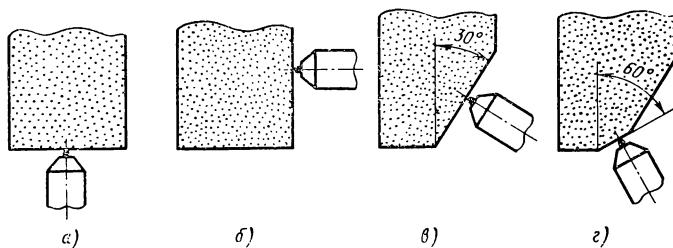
Схема заправки шлифовального круга для шлифования профиля резца:
